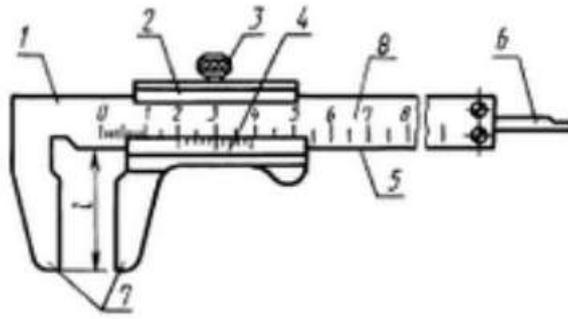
Штангенциркуль односторонний с глубиномером с измерительными поверхностями из твердых сплавов
